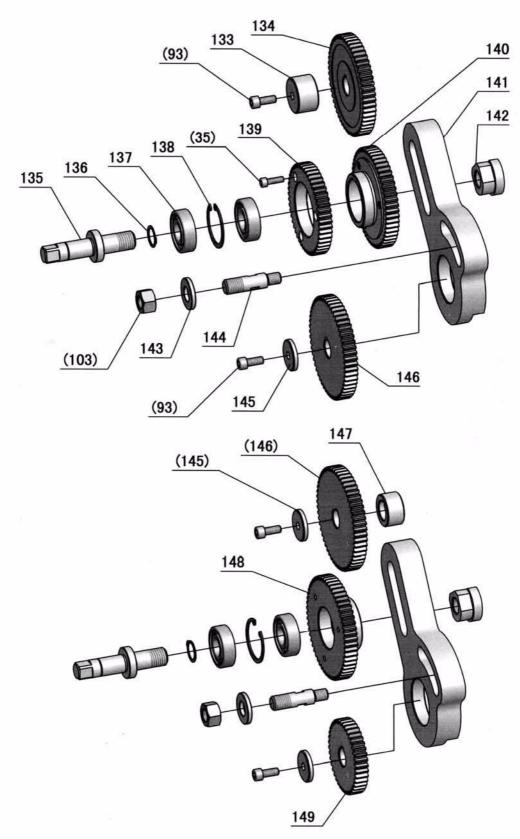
Wechselradgetriebe (metrisch) - Change whell gear (metric)
